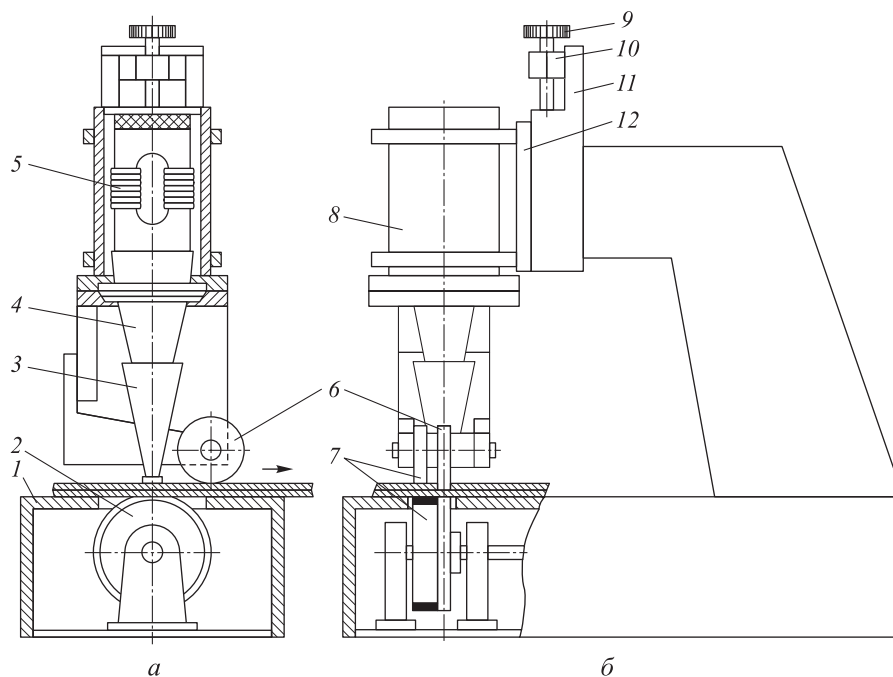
Схема сварочной машины УПШ-12:
